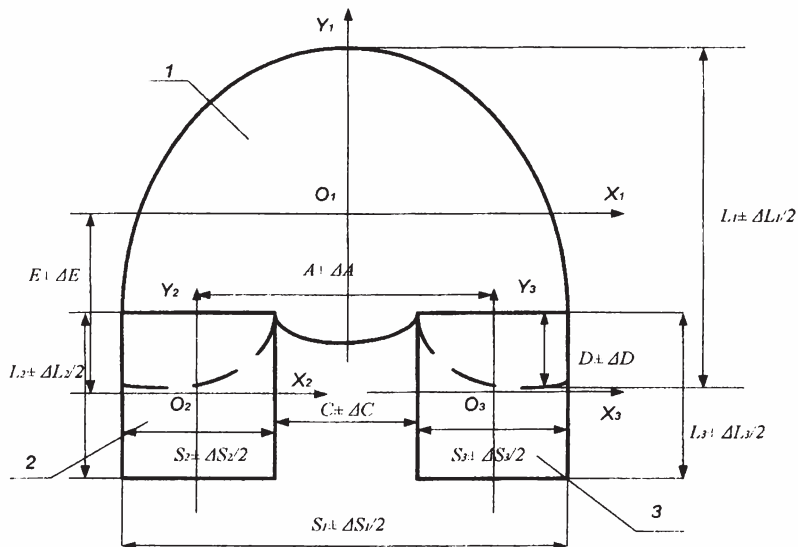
Базування деталей ЗВВ з розташуванням осей координат в умовному центрі деталей
